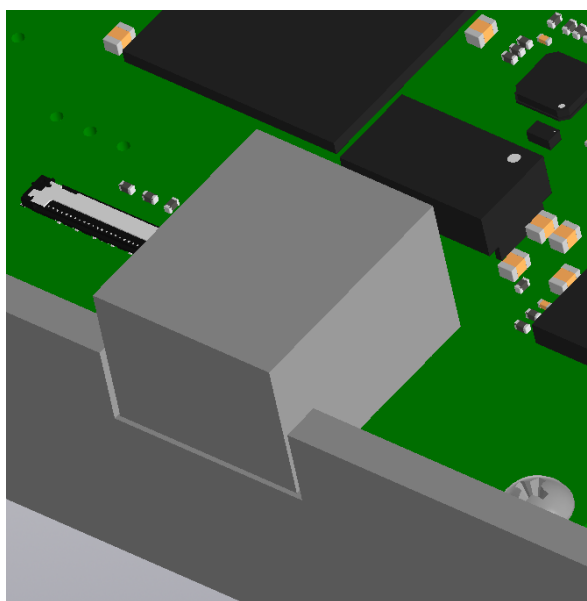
Расположение разъема Ethernet относительно стенки корпуса
